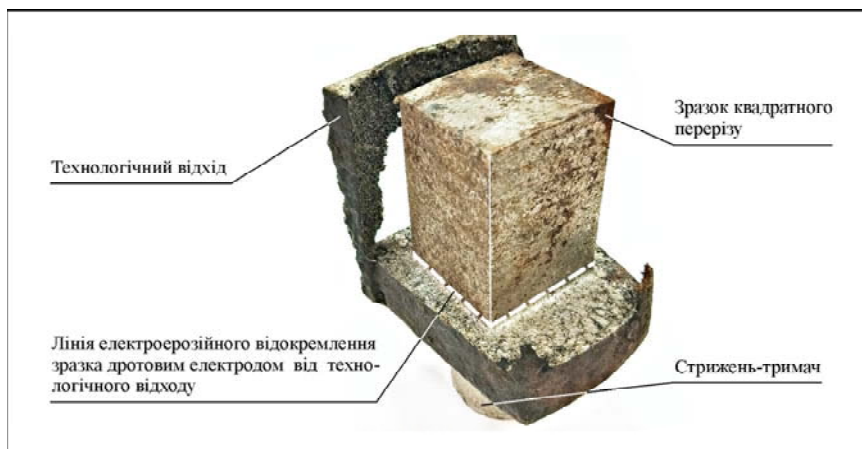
Зразок із ливарної сталі 110Г13Л після РОД
